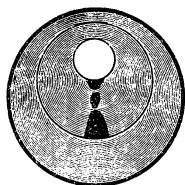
Ствол сверловки чок, подвергавшийся при ремонте обработке поверхности канала ствола (полюровке или шустовке). Прерывистый теневой треугольник показывает выхваты металла
